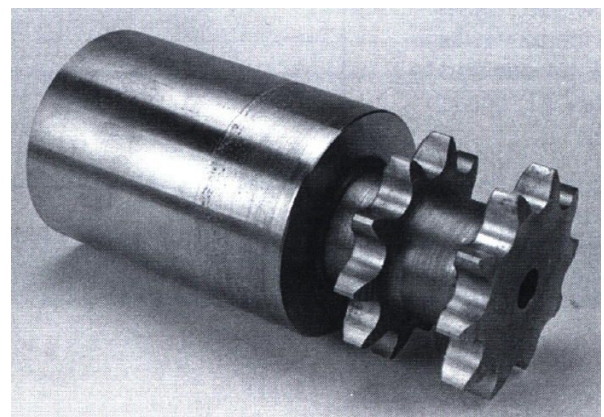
Remplacement de pièces forgées ou coulées par des profilés standards soudés par friction [1].
